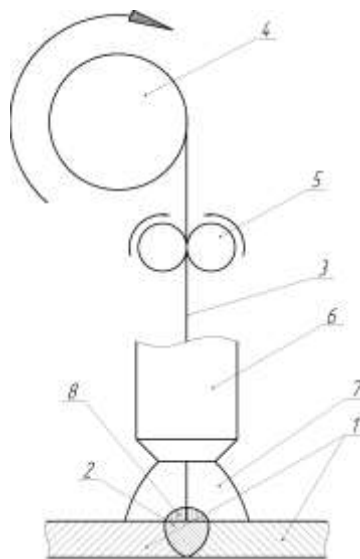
Схема напівавтоматичного зварювання в захисному газі
